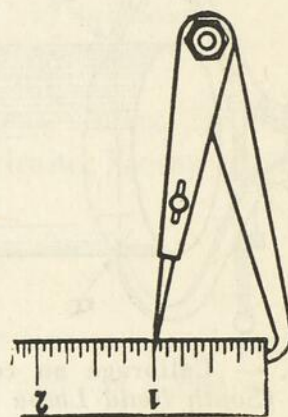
Transfert de dimension (South Bend Lathe Works)
